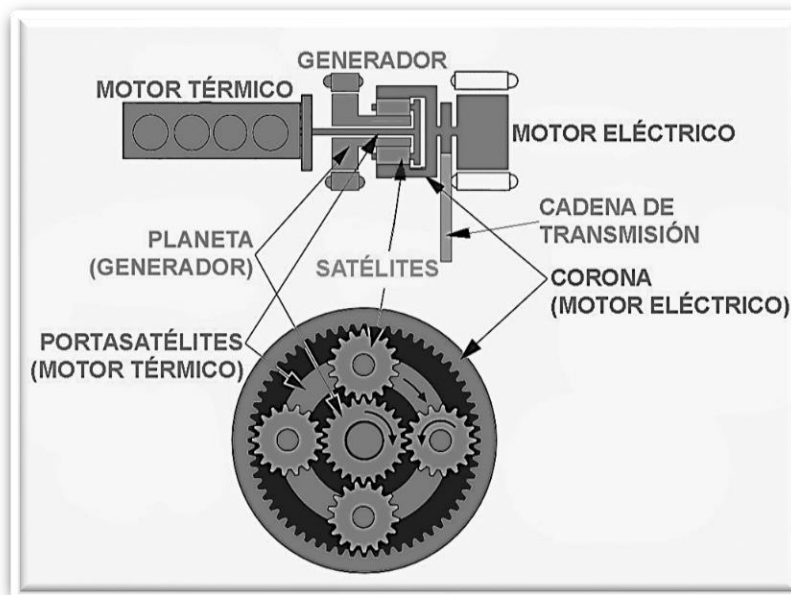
Acoplamiento de engranes planetarios Toyota Prius.
